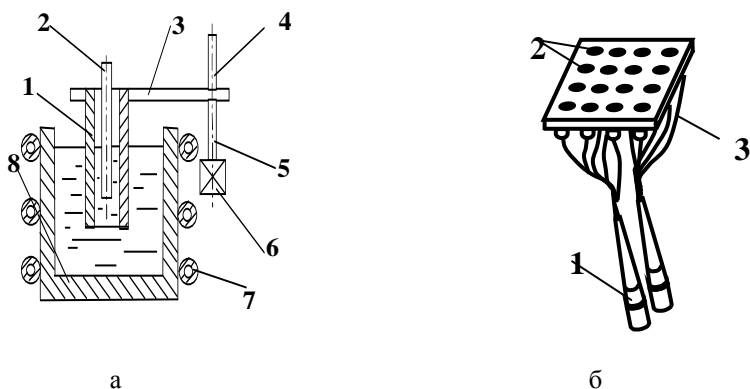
УЗ ванны для длинномерных изделий (а): 1 – трубчатый излучатель, 2 – изделие, 3 – пластинчатый волновод, 4, 5 – волноводы, 6 – УЗ преобразователь, 7 – нагреватель; 8 – ванна; для пайки и лужения миниатюрных изделий (б): 1 - преобразователи; 2 – паяльные тигли, 3 – гибкие волноводы
